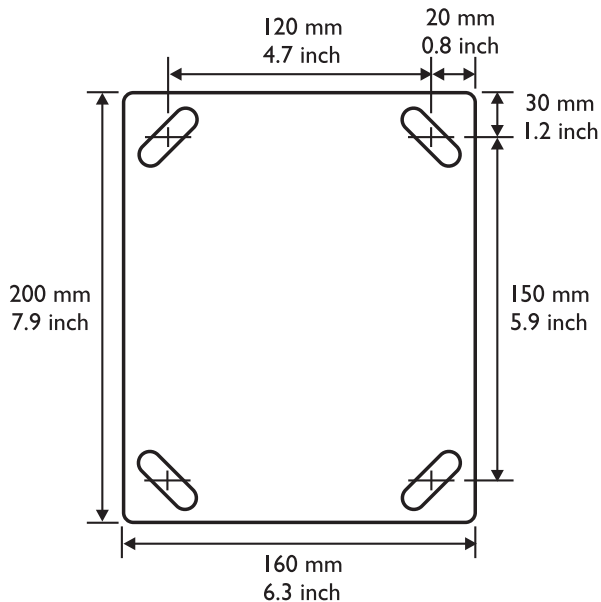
Suporte de montagem na parede LBB 3414/00 mostrando dimensões e o padrão de perfuração
